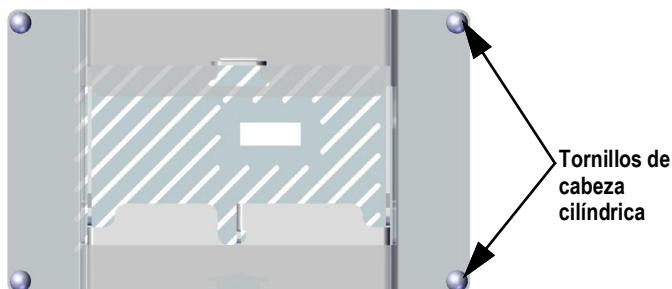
Posición de los tornillos en el soporte del carril DIN
